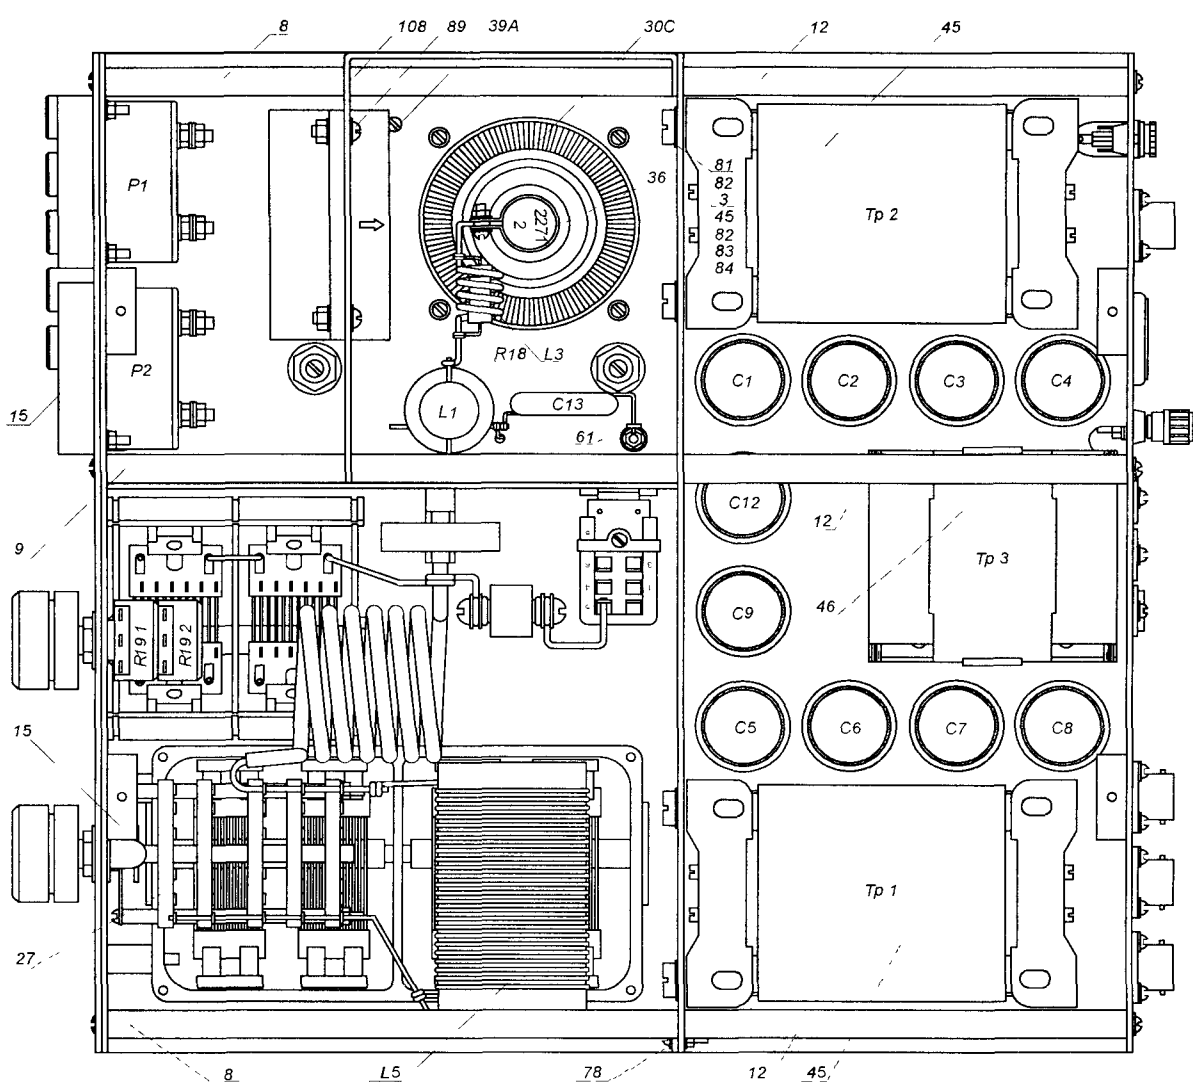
D. Сборочный чертеж усилителя DVA-300D Вид сверху со снятой верхней крышкой
